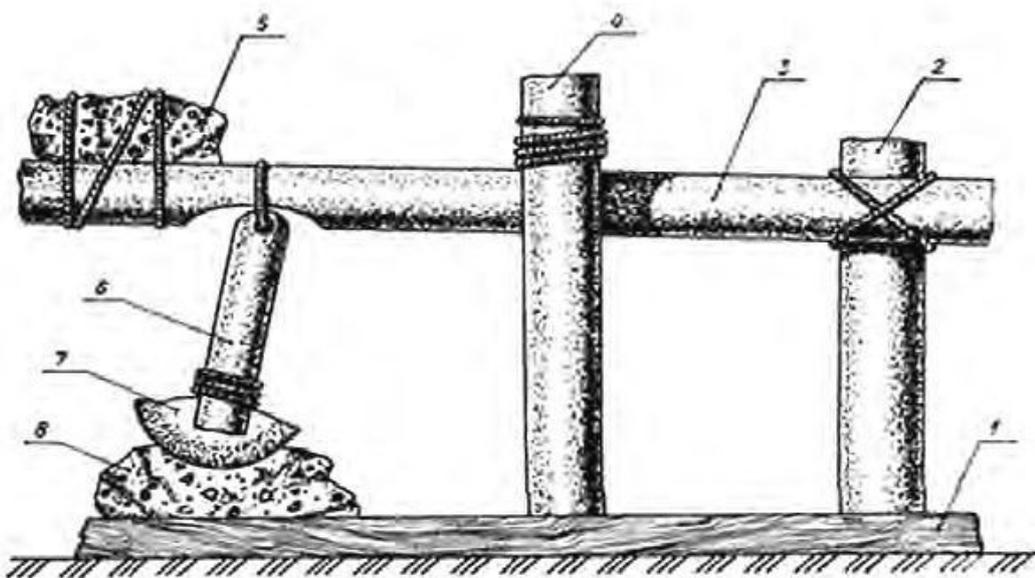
Первобытный камнераспилочный станок (реконструкция). 1 – фундаментная доска, 2 – стойка-колонна, 3 – горизонтальная балка, 4 – вертикальные направляющие балки, 5 – пригруз (камень), 6 – качающаяся деревянная подвеска, 7 – рабочий инструмент (пластина кремня), 8 – распиливаемый камень [22]
